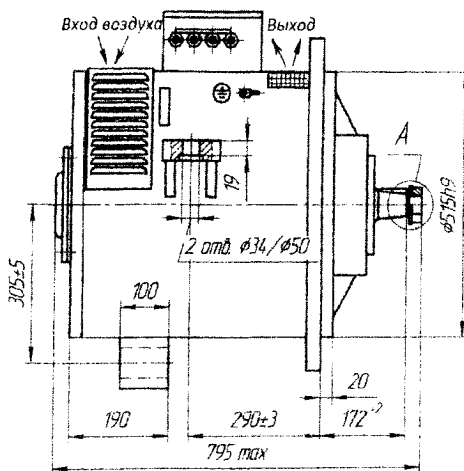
Общий вид тягового двигателя ДТН-45
